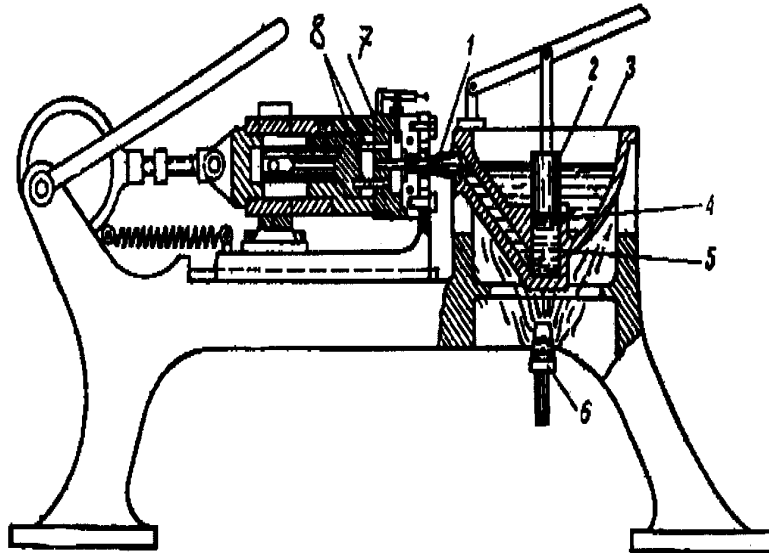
Поршнева машина з гарячою камерою пресування:
